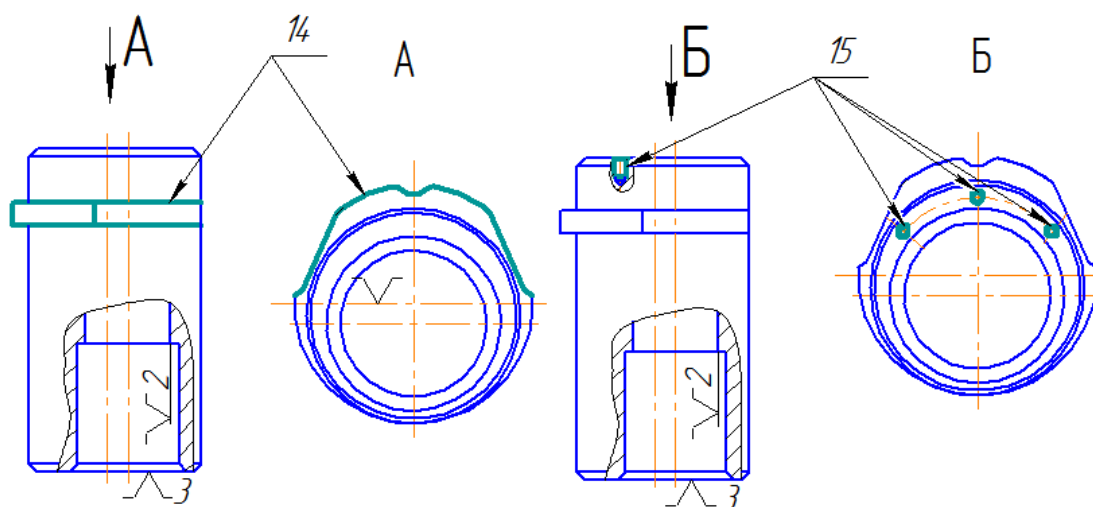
Эскиз фрезерной операций с ЧПУ 045 (Установ А)
